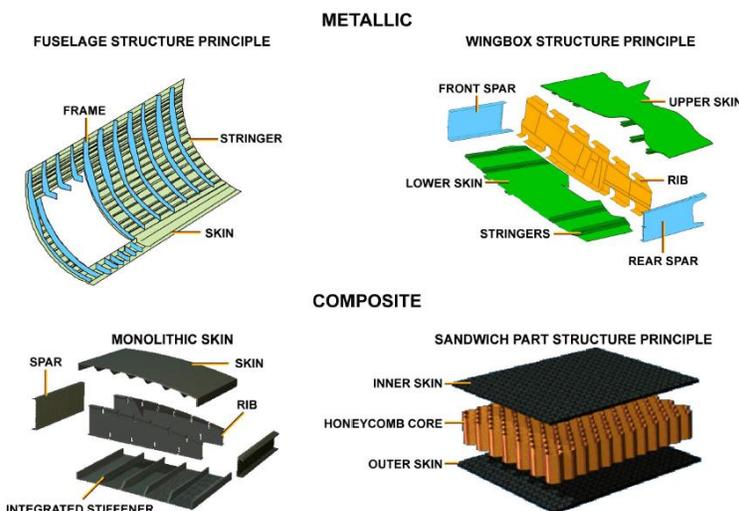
Estructura tipo sándwich frente a una estructura metálica.
